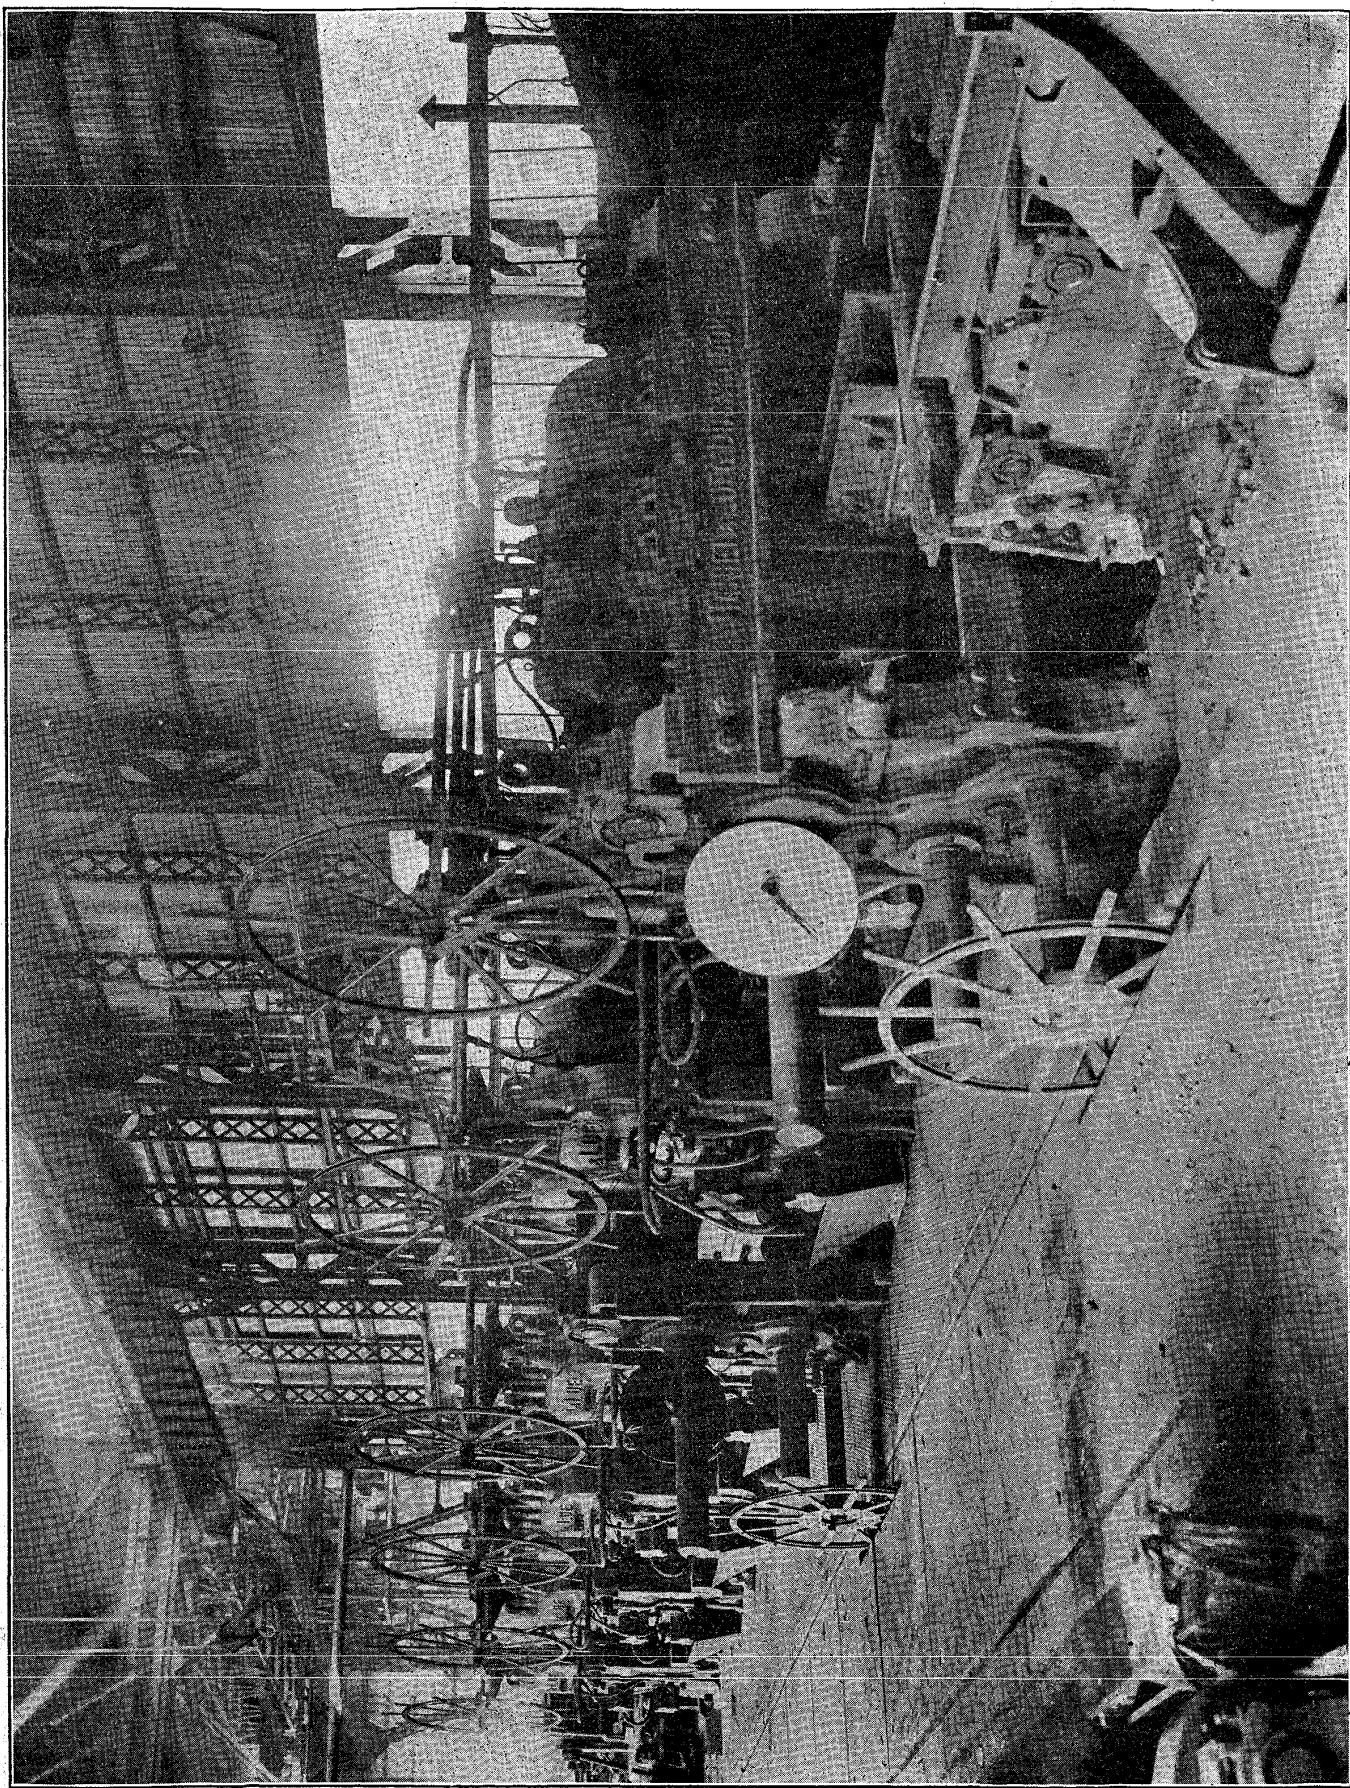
第6分塊工場 第2號連續ロール機 (シートバー及45-60 mm 角鋼片用) 450 mm continuous billet and sheet bar mill
